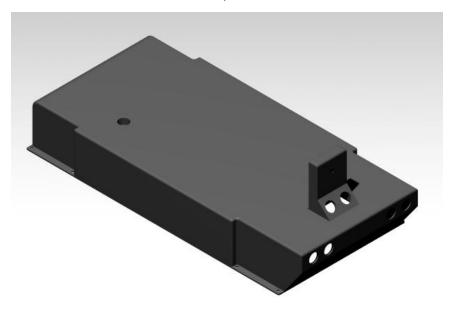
Carcaça Superior- Após impressão 3D.
